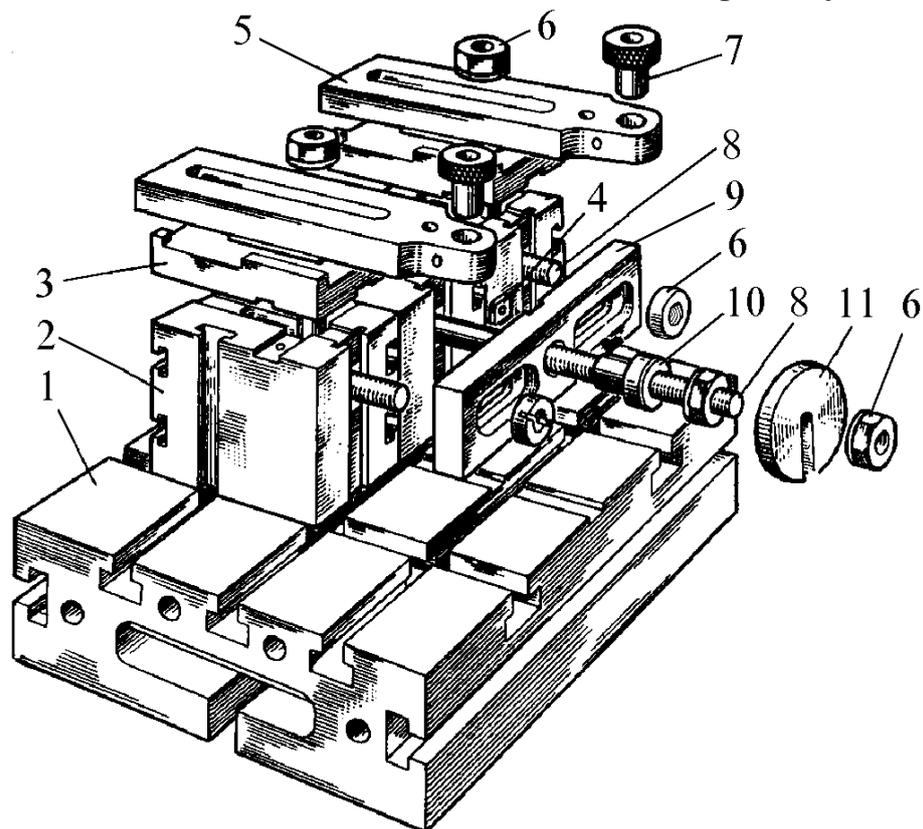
Внешний вид универсально-сборного приспособления для сверления отверстий: базовая плата; 2 - опора; 3 - направляющая опора; 4 - шпонка; 5 - кондукторная планка; 6 - гайка; 7 - кондукторная втулка; 8 - болт; 9 - опорная планка; 10 - установочный палец; 11 - быстро-съемная шайба
